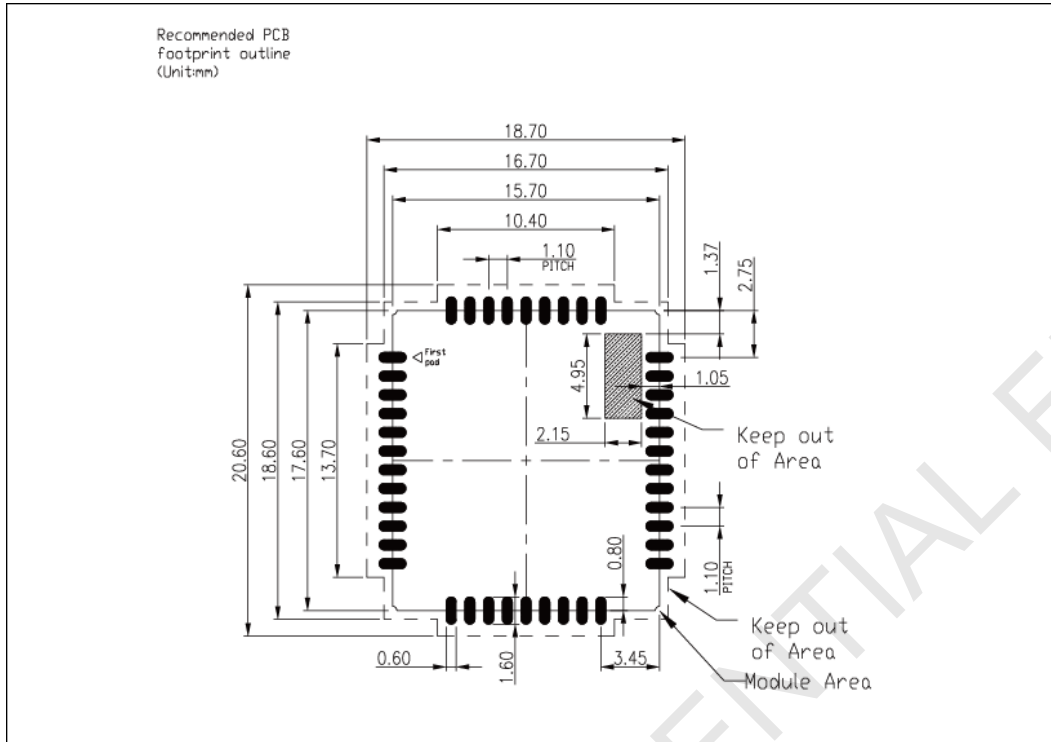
推荐 PCB 封装尺寸 (单位: 毫米)
